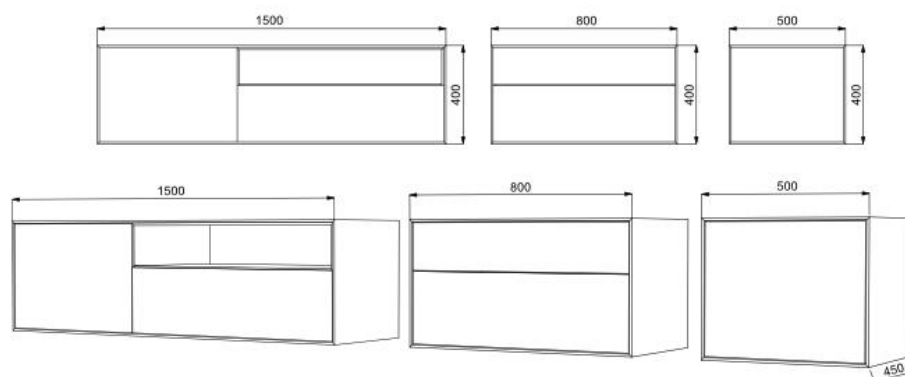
Korpus pro prototyp komody Obr.46 Výsuvný mechanismus
